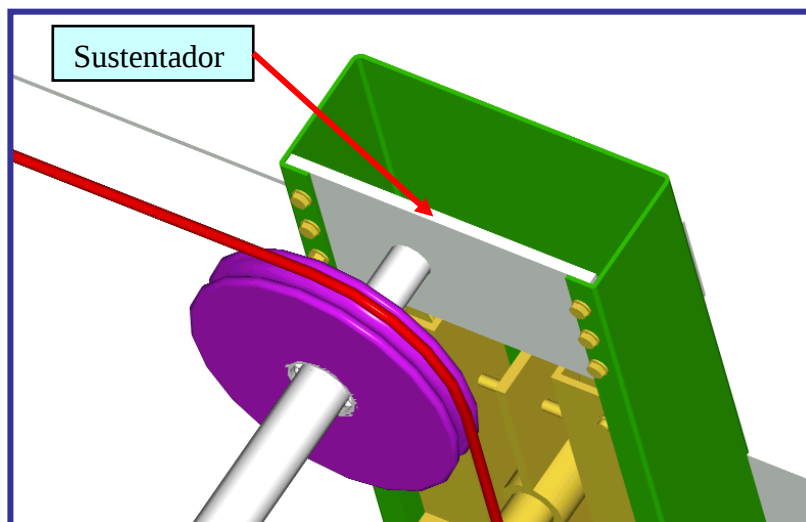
Sustentador do eixo das roldanas da parte superior do Equipamento de Movimentação Vertical.
